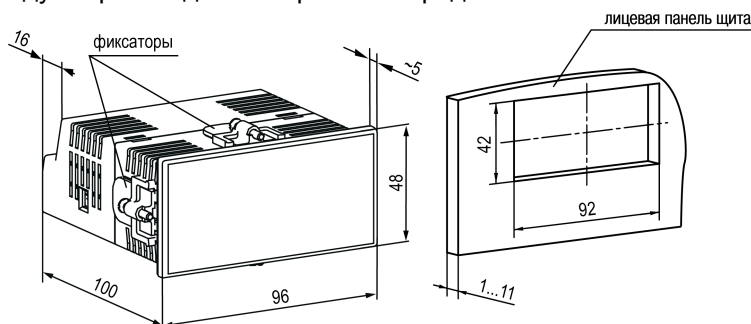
Габаритные размеры корпуса Щ2 и монтажного отверстия в щите
